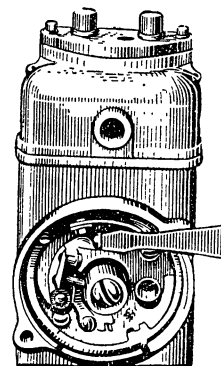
Регулировка зазора в контактах прерывателя магнето М-10А.
